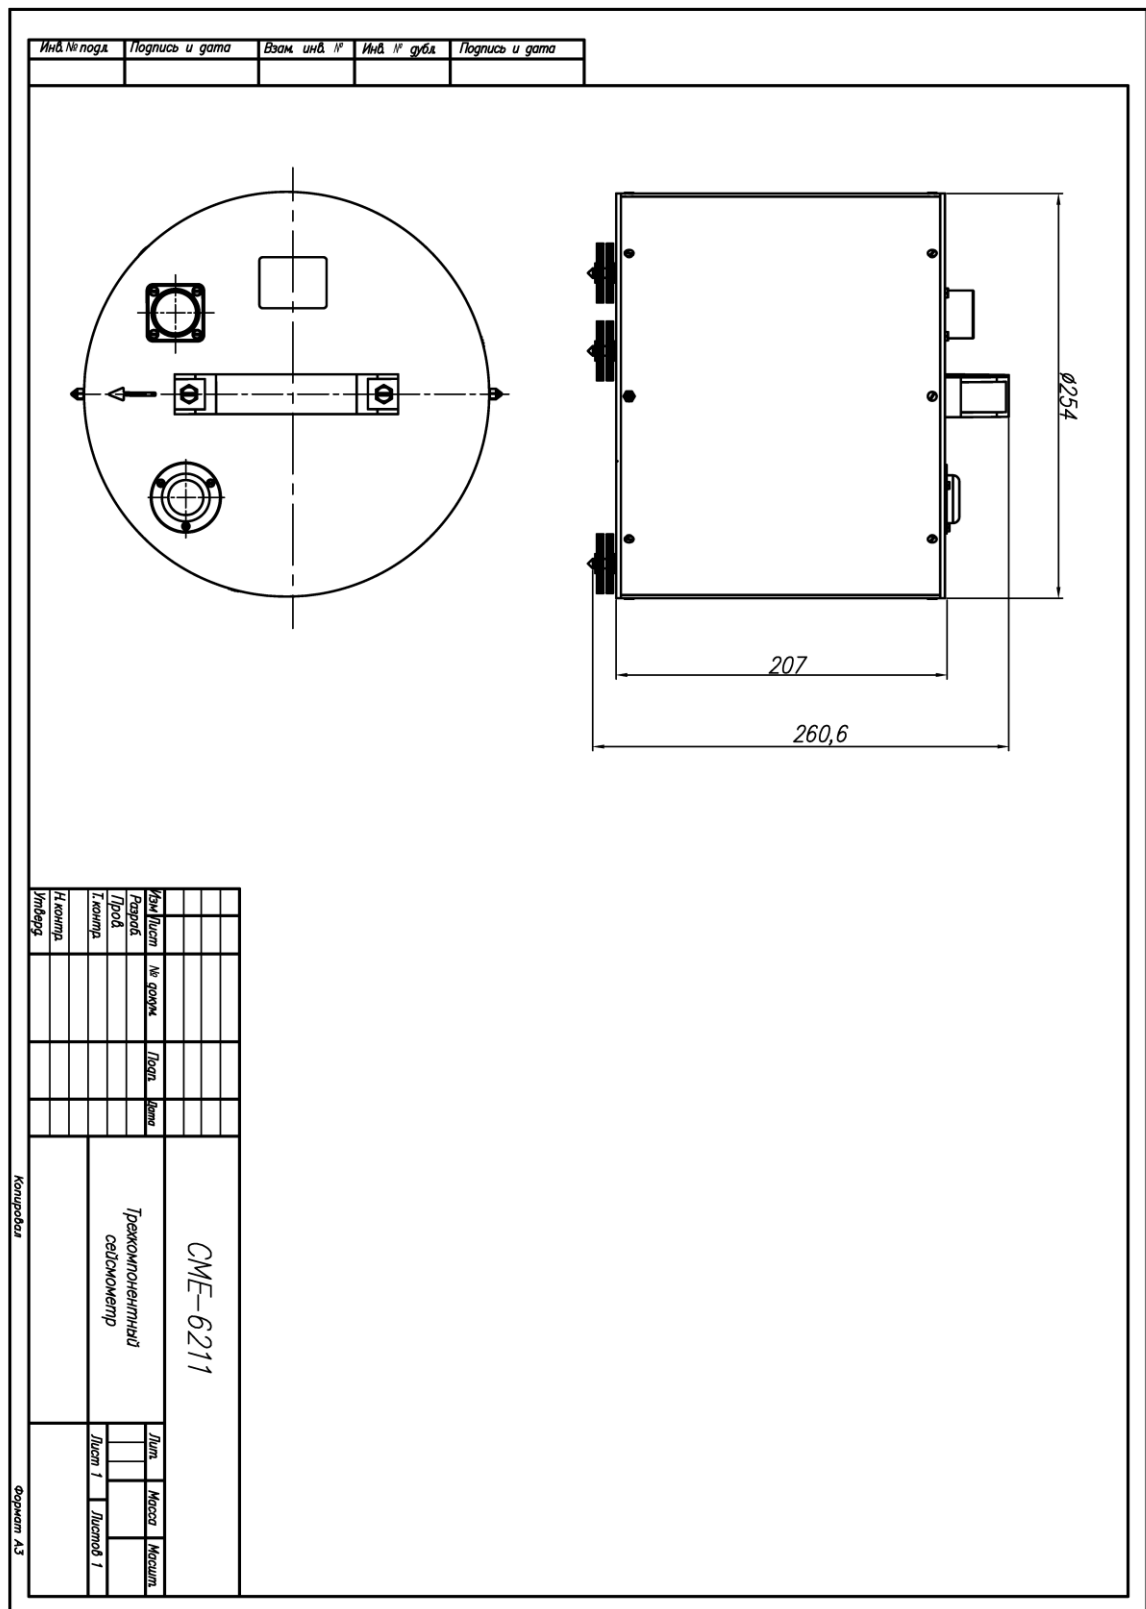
Габаритный чертеж сейсмометра СМЕ-6211.
